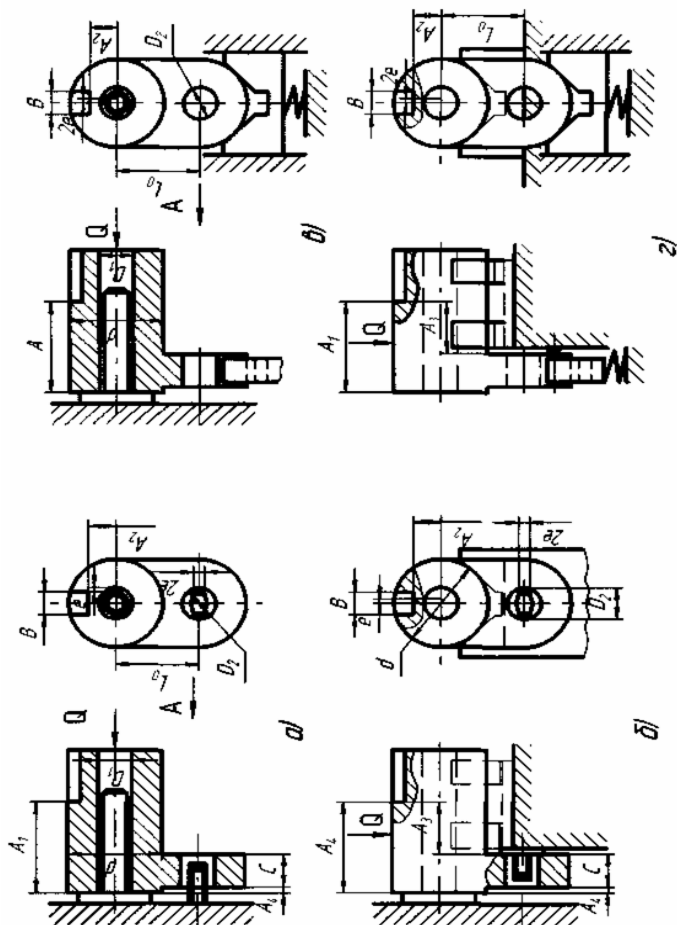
Схеми встановлення заготовки при обробці шпонкового пазу
